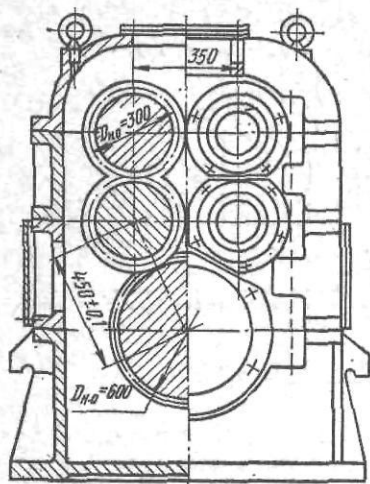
Комбинированная шестеренная клетка-редуктор 20-валкового стана 1200 конструкции ВНИИметмаша
